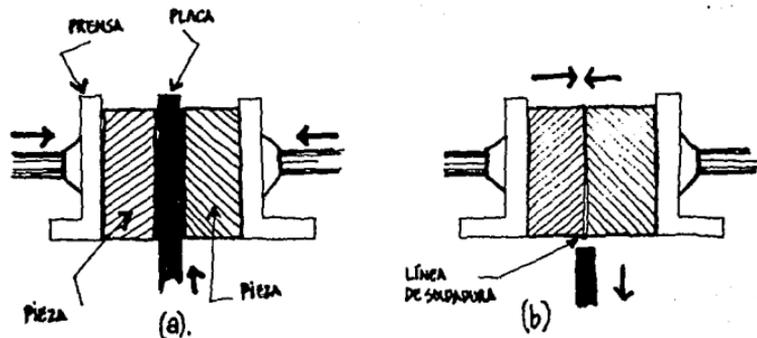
Las dos estaciones de soldadura por placa caliente a).- Aplicaciones de la placa b).- Presión y enfriamiento
